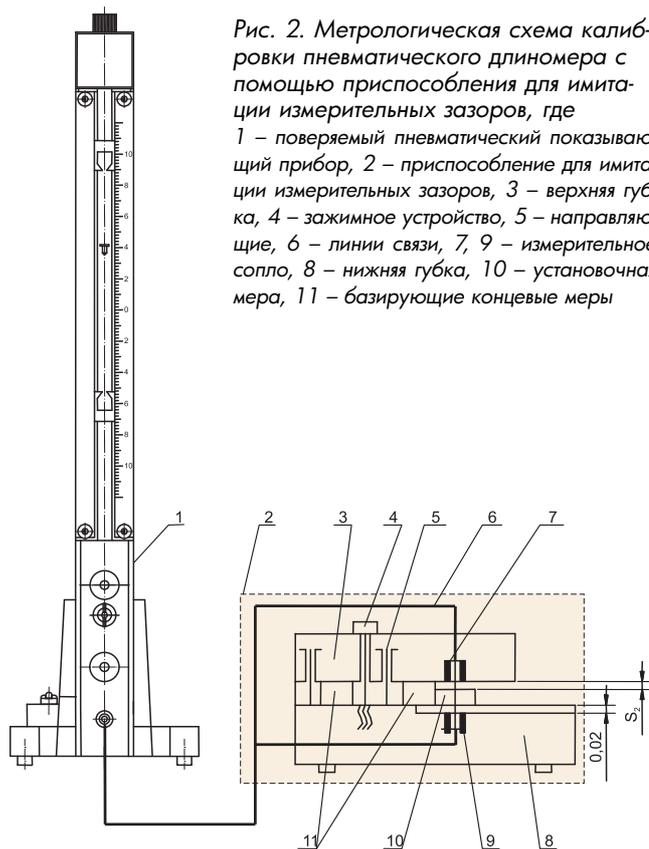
Метрологическая схема калибровки пневматического длиномера с помощью приспособления для имитации измерительных зазоров, где 1 – поверяемый пневматический показывающий прибор, 2 – приспособление для имитации измерительных зазоров, 3 – верхняя губка, 4 – зажимное устройство, 5 – направляющее, 6 – линии связи, 7, 9 – измерительное сопло, 8 – нижняя губка, 10 – установочная мера, 11 – базирующие концевые меры
